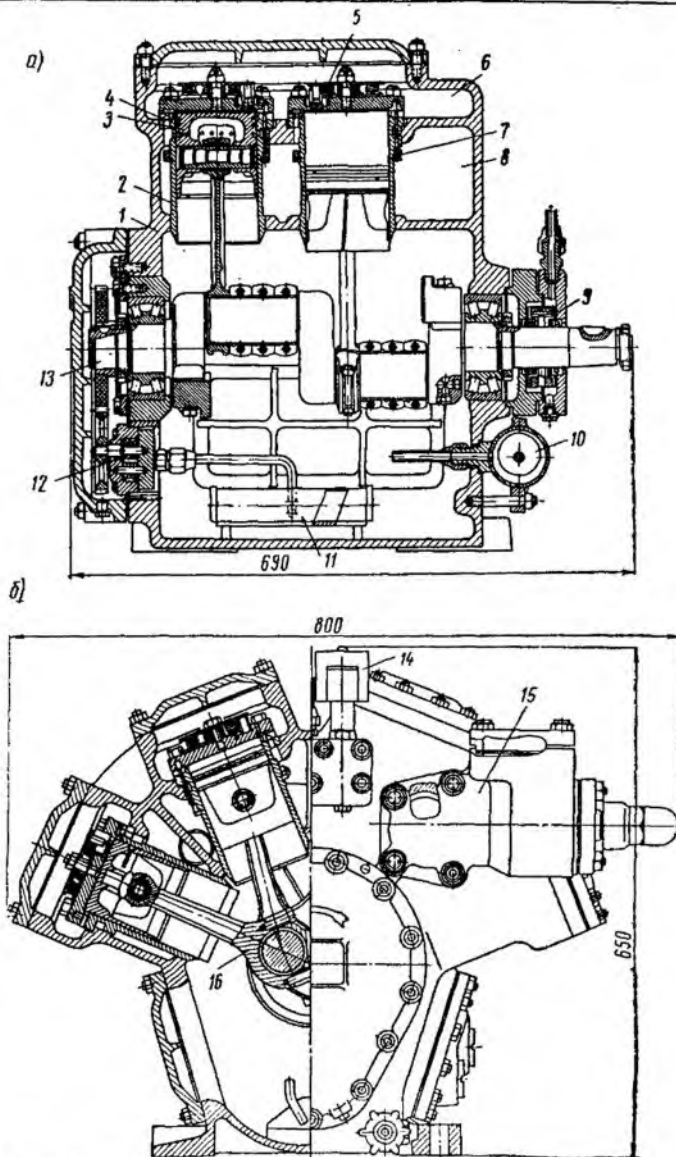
Фреоновый непрямоточный восьмицилиндровый компрессор ФУУ-80:
